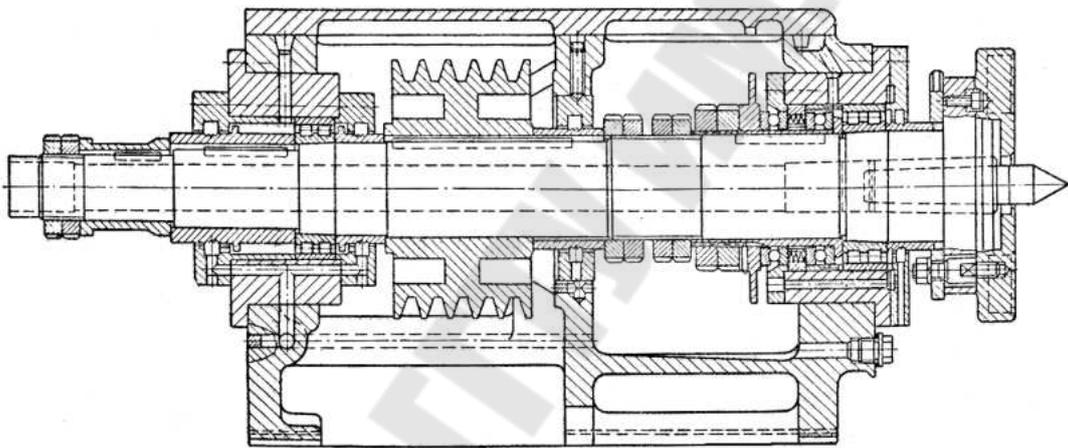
Шпиндельный узел токарного станка с упорными шарикоподшипниками
